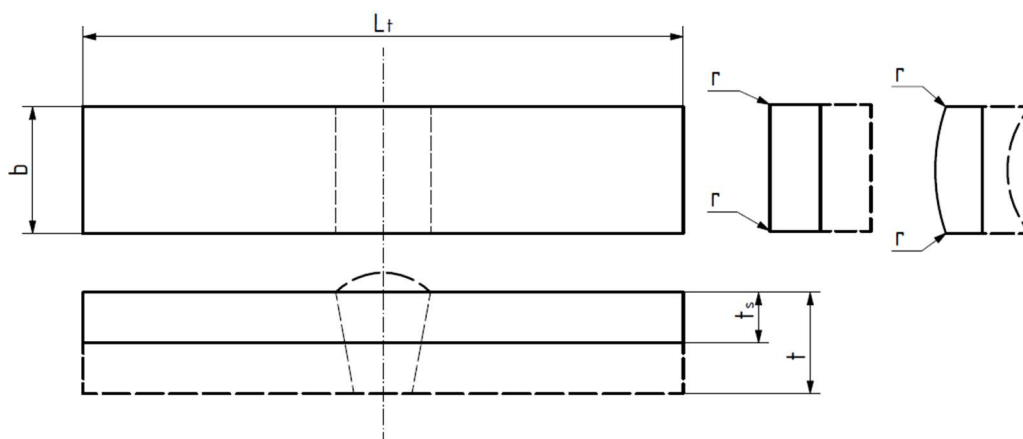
Detail zkušební tyče po zkoušce ohybem
